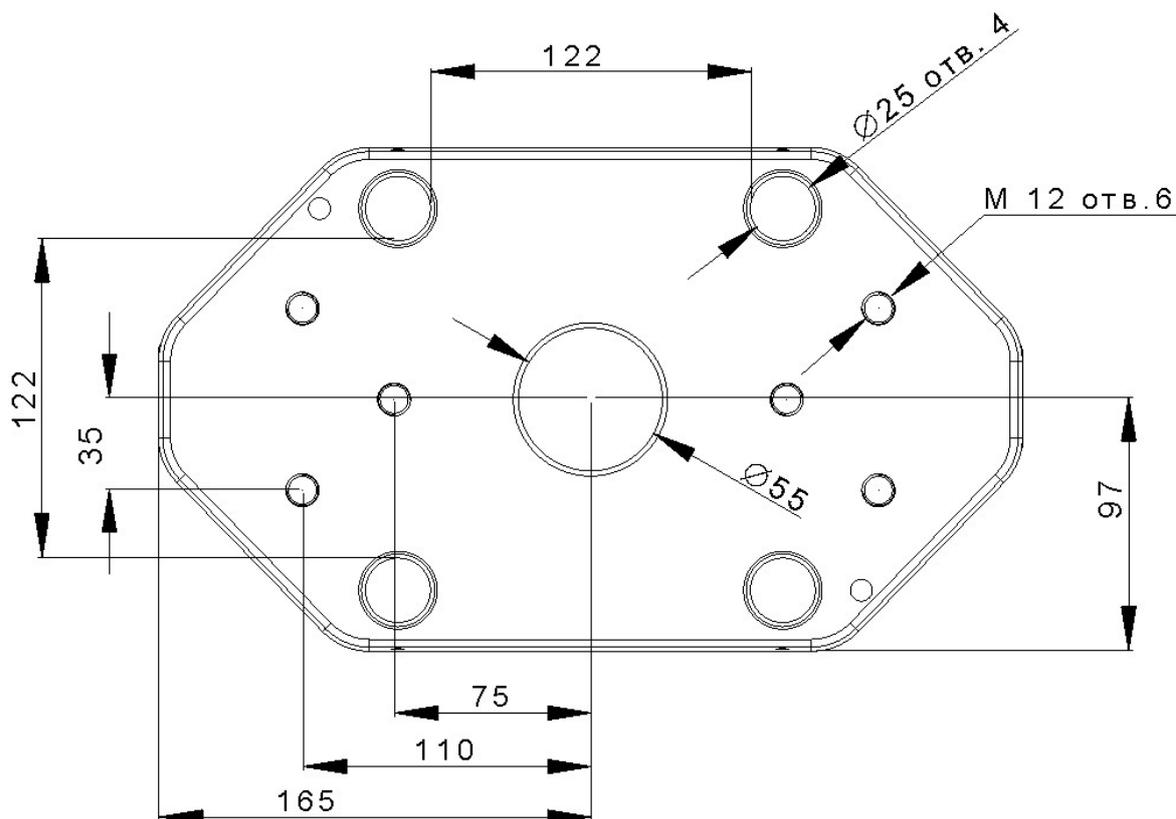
Плита крепления пресс-форм (левая) для «Formolder IMS-55»
